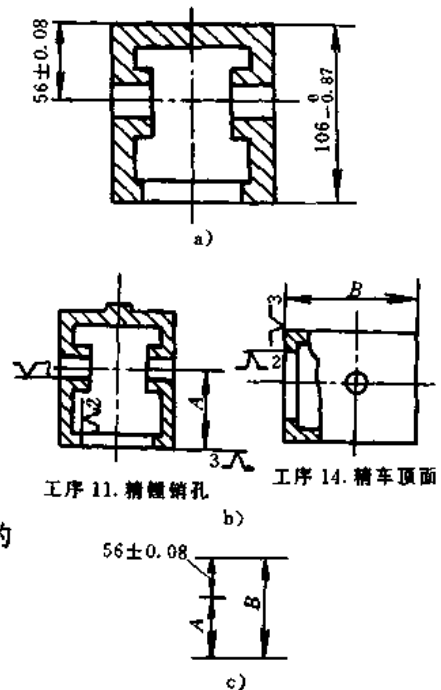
基准不重合时工序尺寸与公差确定
